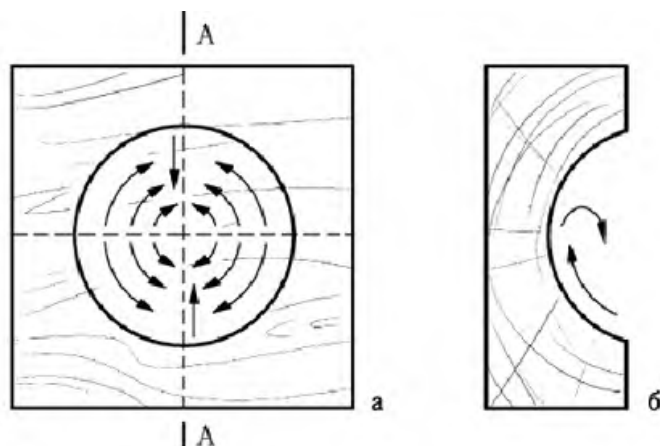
Выполнение резьбы вогнутой выемки на пласти заготовки первым способом (стрелками показано направление движения инструмента)
